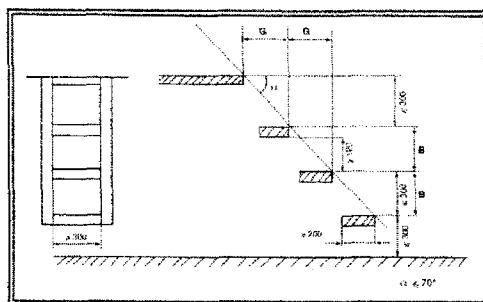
Dimensioni dei mezzi d'accesso alla zona di carico
